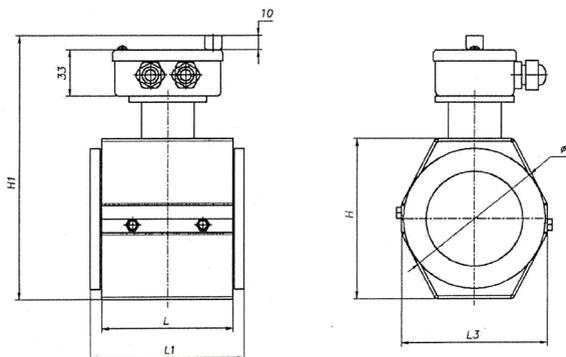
Габаритные и установочные размеры ПРПЭ типа ПРН
